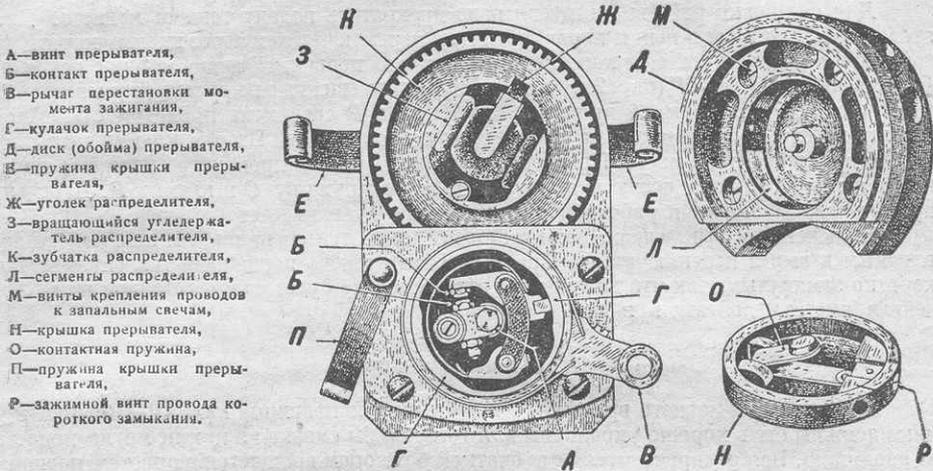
Магнето «Бош». Вид со стороны прерывателя. Крышки прерывателя и распределителя сняты.
